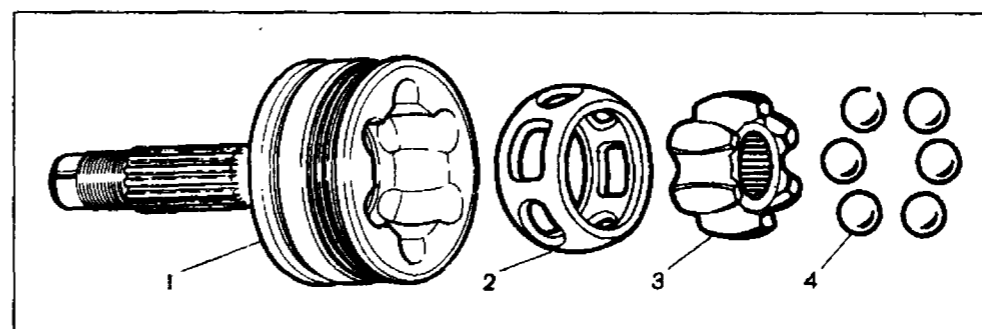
Детали наружного шарнира: 1 — корпус шарнира; 2 — сепаратор; 3 — обойма; 4 — шарики
